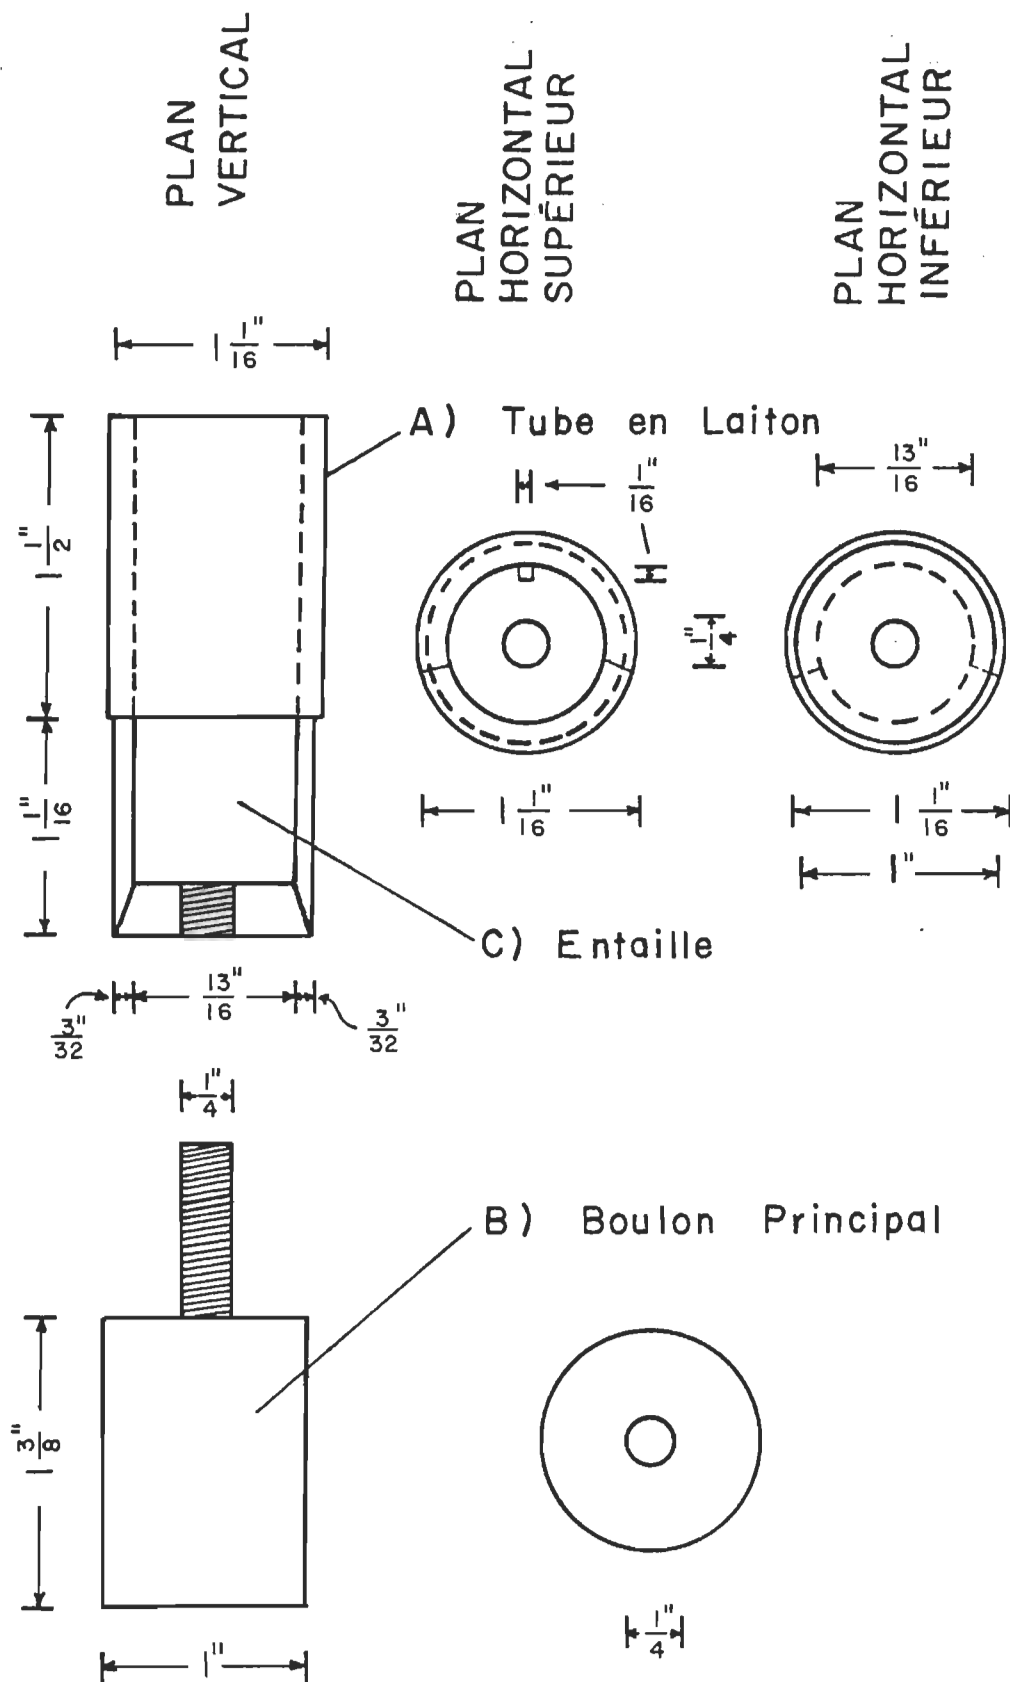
Plan détaillé de la section e comprenant le tube de laiton et le boulon principal.
